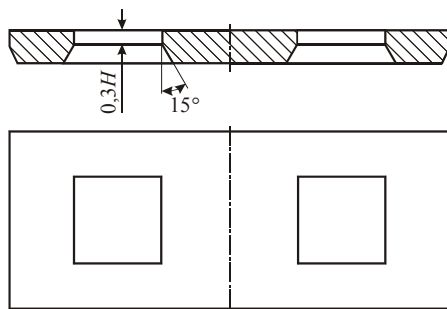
Типова конструкція вирубного штампа нескладної форми
